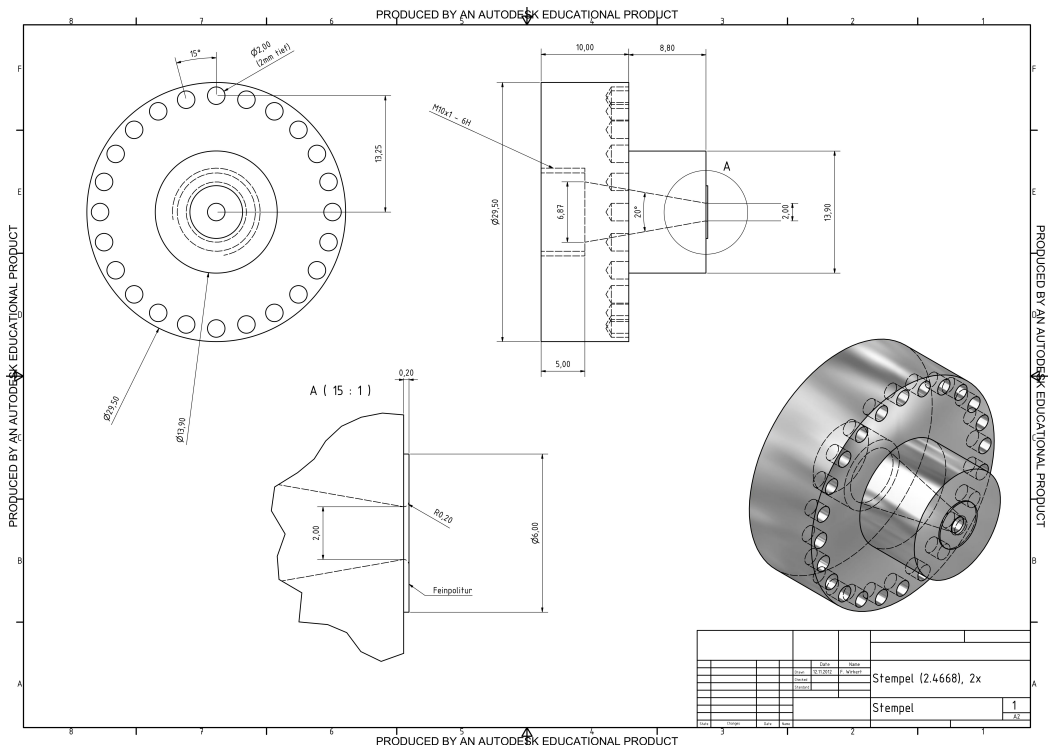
Technische Zeichnung Diamant-Stempel
